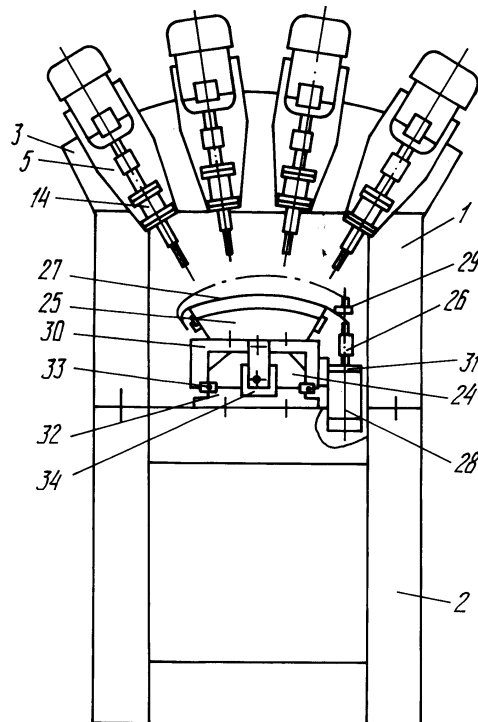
Верстат агрегатний для свердління накладок
